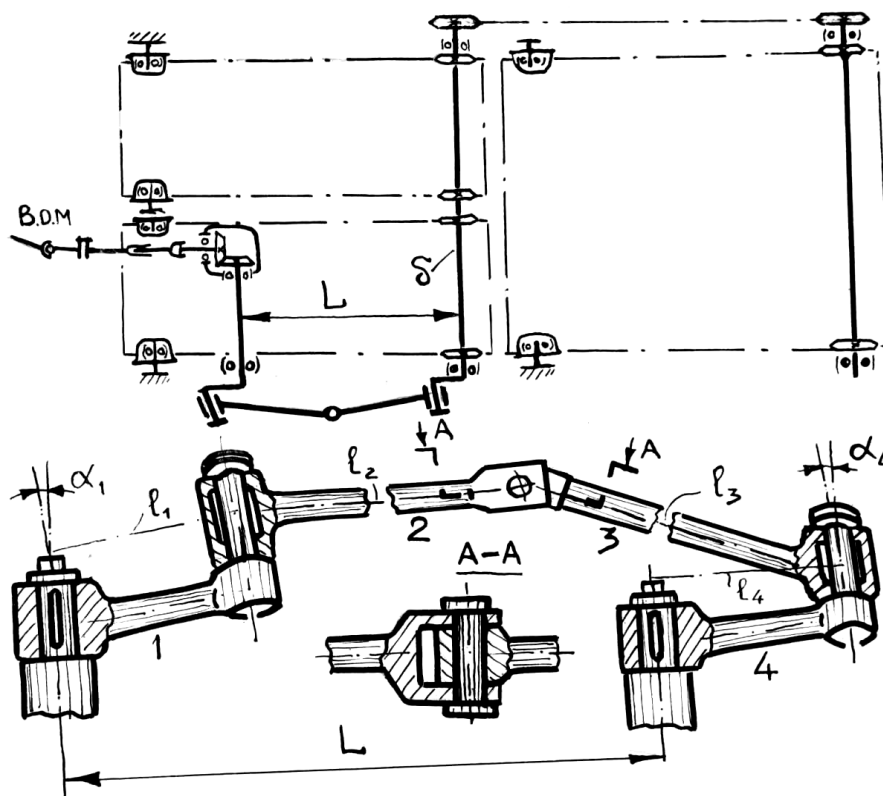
Схема привода элеваторов картофелеуборочного комбайна
